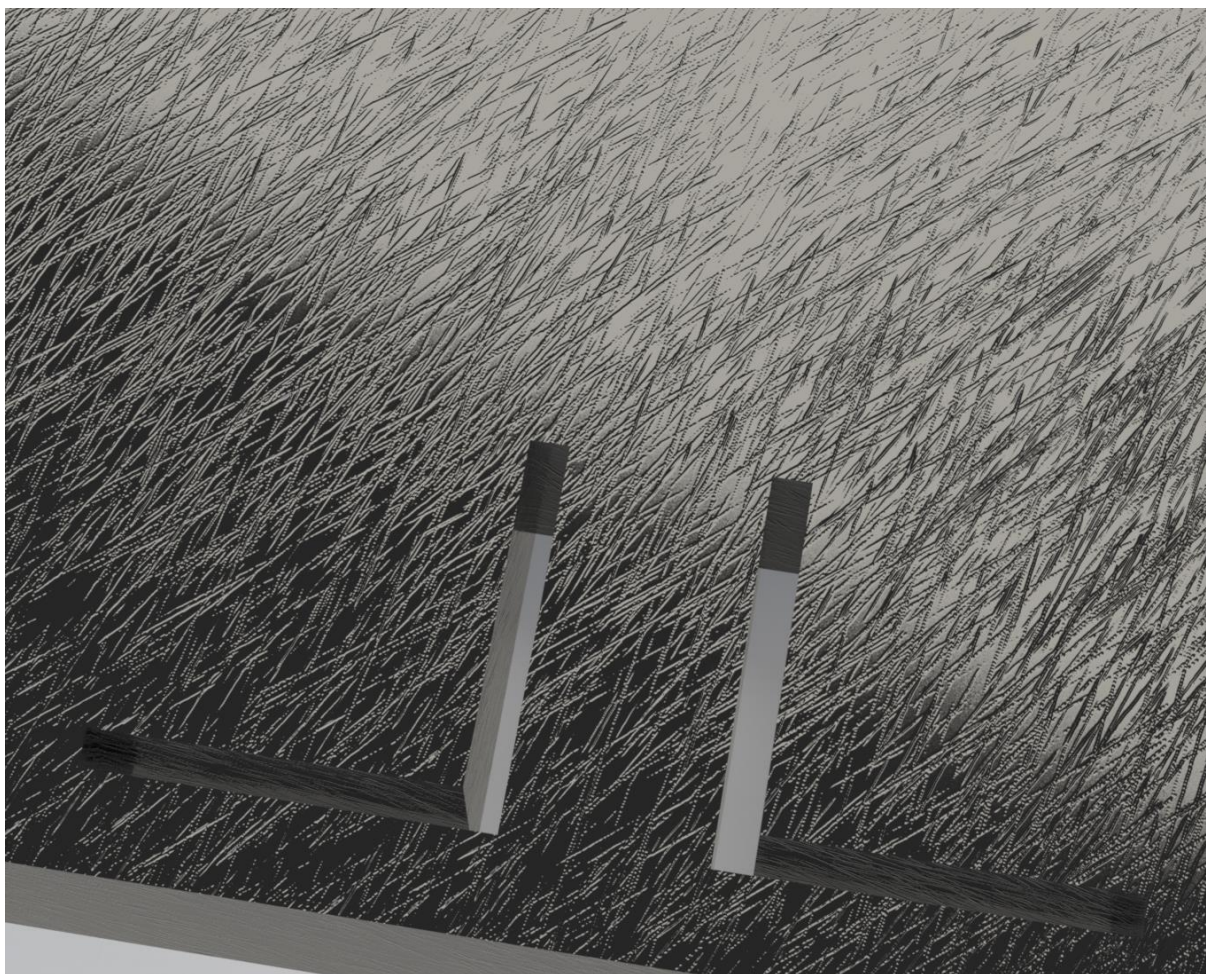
Detalle hendiduras para anclar cajas a la plataforma base
